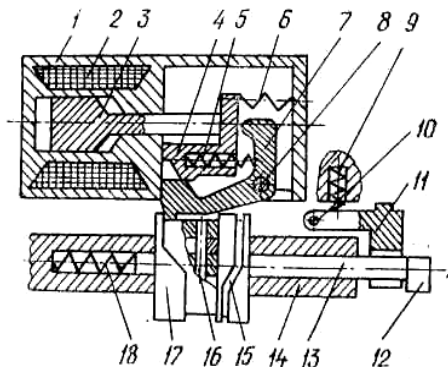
Спусковий механізм кулемета ЯкБ-12,7
